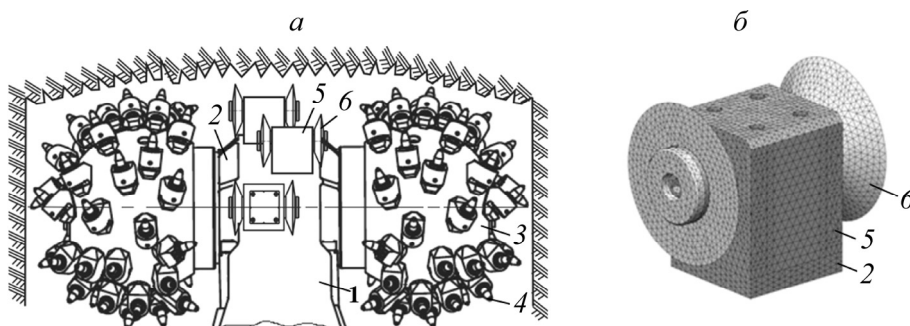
Конструкция стреловидного исполнительного органа с аксиальными резовыми коронками: *а* — конструктивная схема; *б* — конечно-элементная модель четырехгранной призмы с двумя дисками; 1 — стрела; 2 — раздаточный редуктор; 3 — коронка; 4 — резец; 5 — четырехгранная призма; 6 — дисковый инструмент
